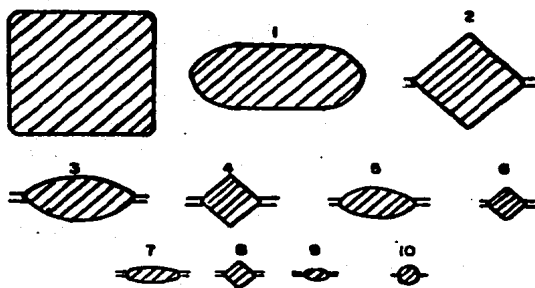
Número de pasadas y secuencia en la reducción de la sección transversal de un facho, hasta barra redonda.
